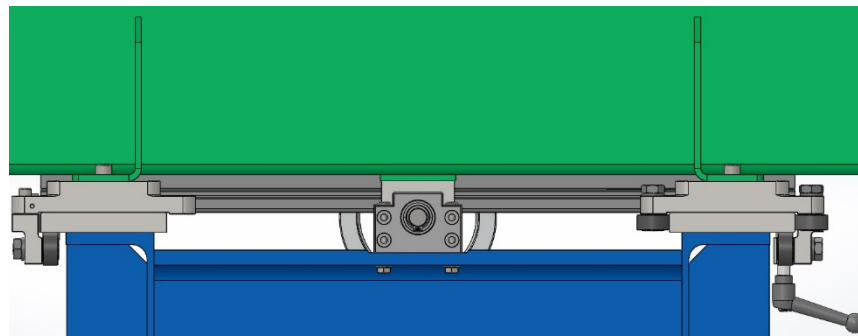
Detalle de la disposición del conjunto de guiado
